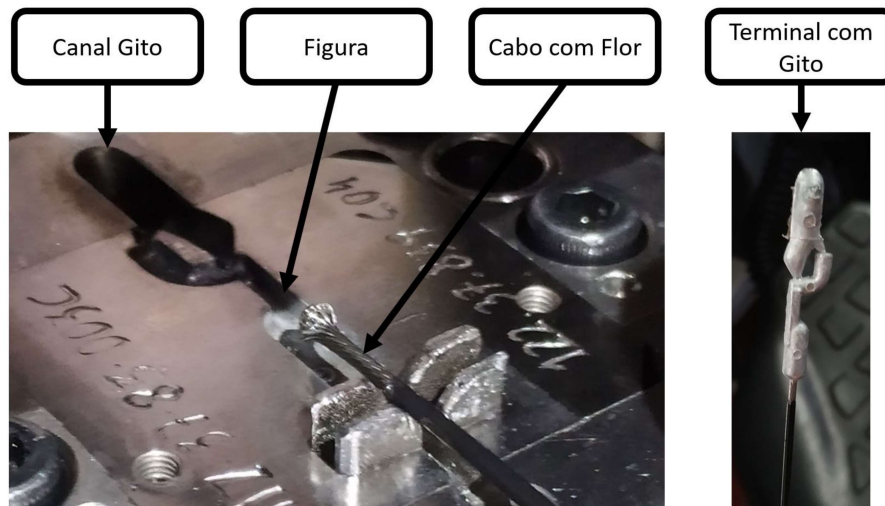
Cabo no molde antes da injeção (esquerda) e após a injeção com gito (direita)
